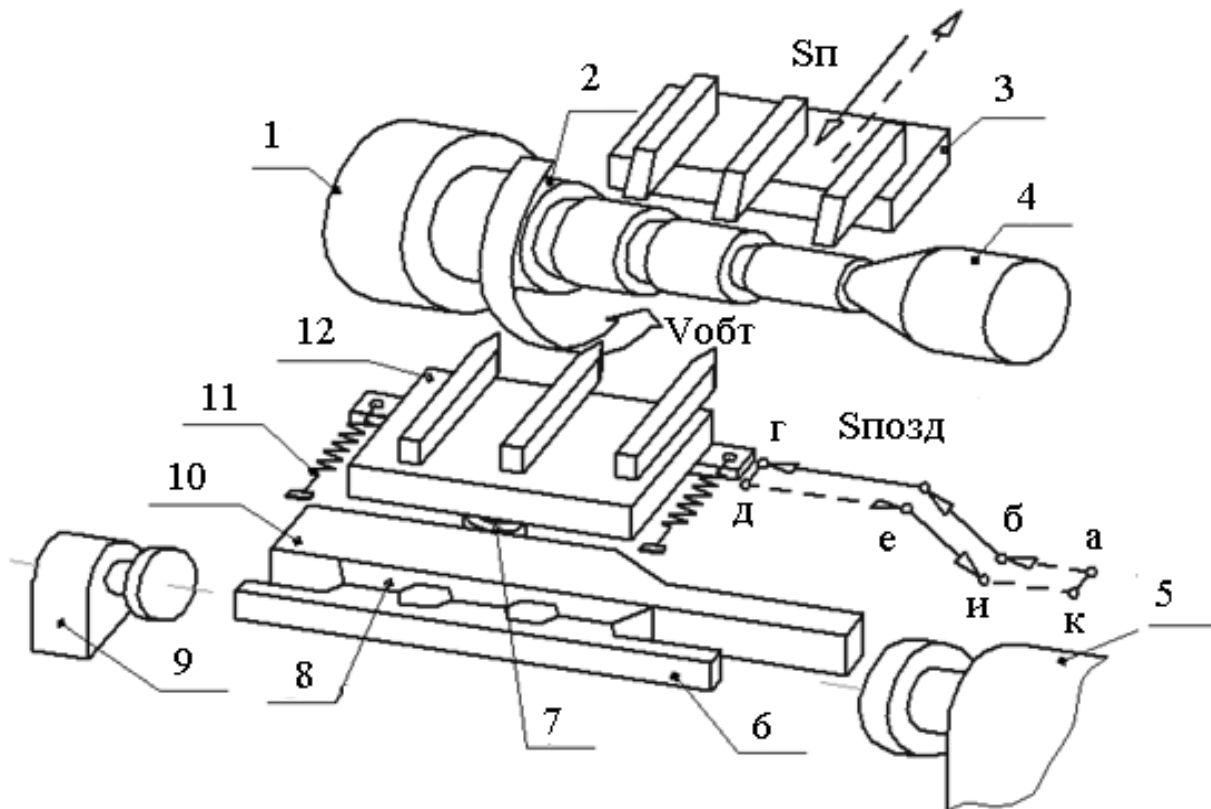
Схема роботи багаторізцевого напівавтомата
